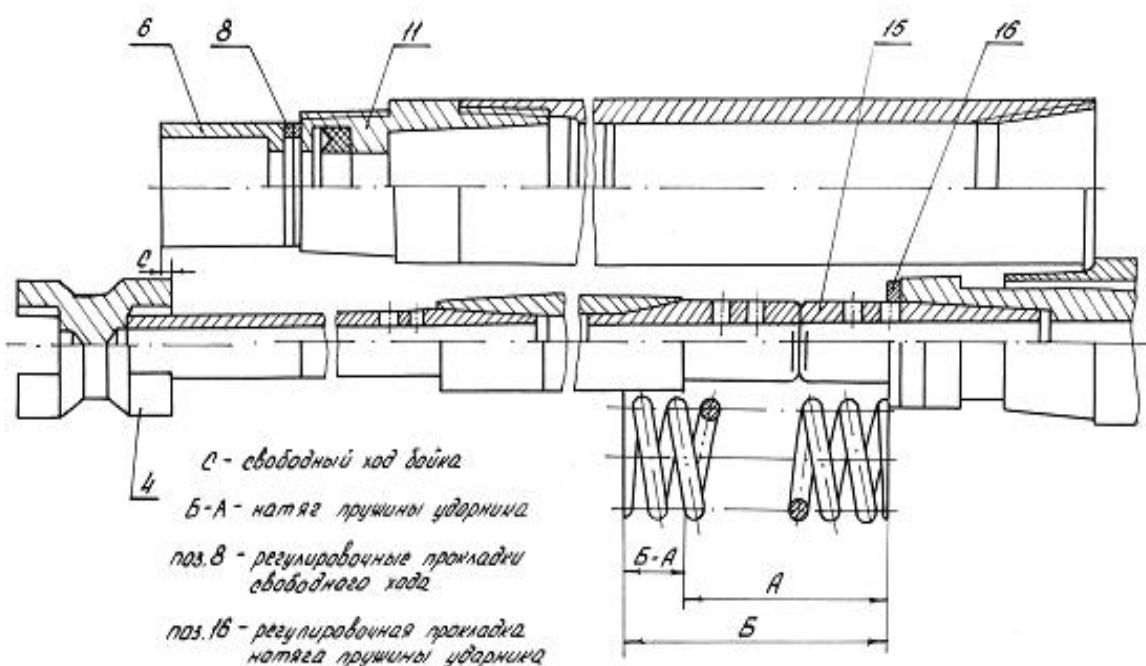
Схема для проведения регулировки свободного хода бойка и натяга пружины бойка:
